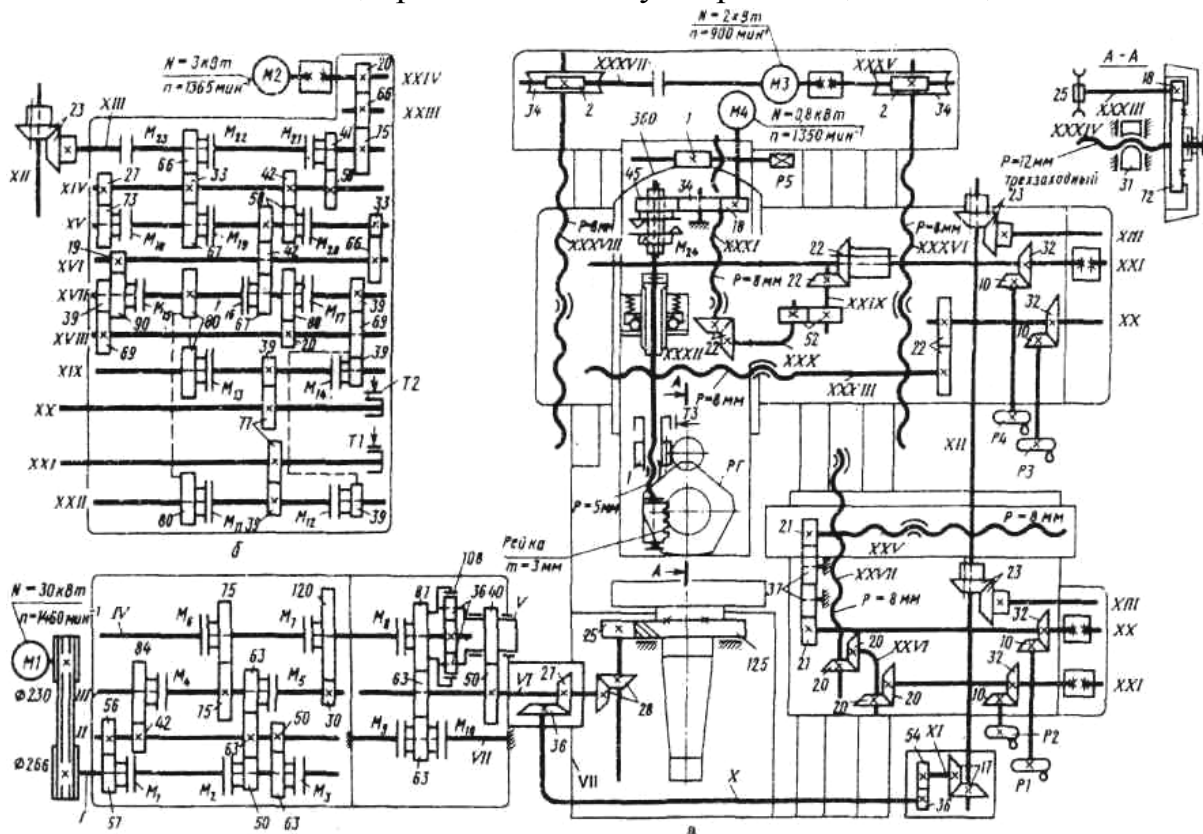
Кинематическая схема токарно-карусельного станка модели 1512
